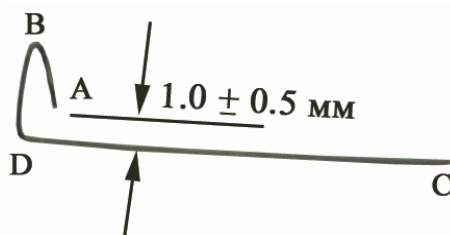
Форма вольфрамовой заготовки для датчика
